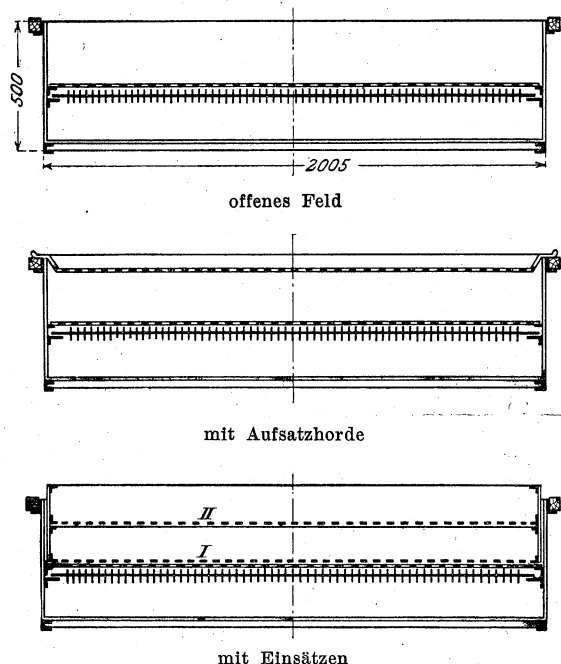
bis 9. Querschnitt durch ein Darrfeld.
